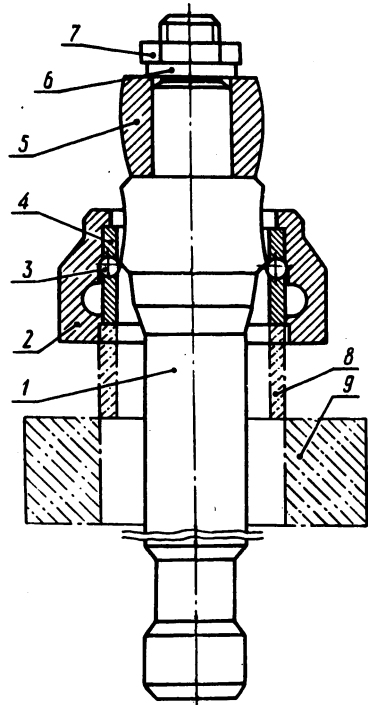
Устройство для совмещения в один технологический переход процессов запрессовки втулок и калибровки в них отверстий.
